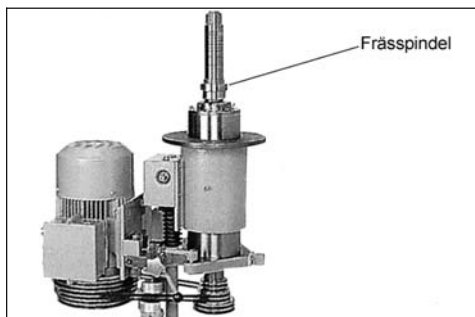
Fräsmotor mit Doppelriemenantrieb
